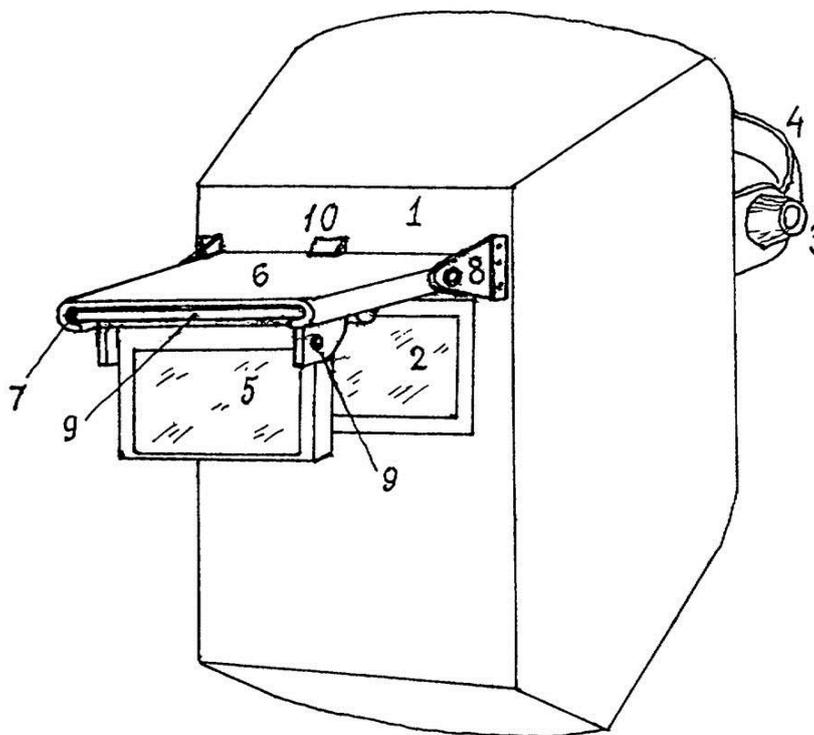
Защитная маска сварщика, пат. № 2309714 [34].
